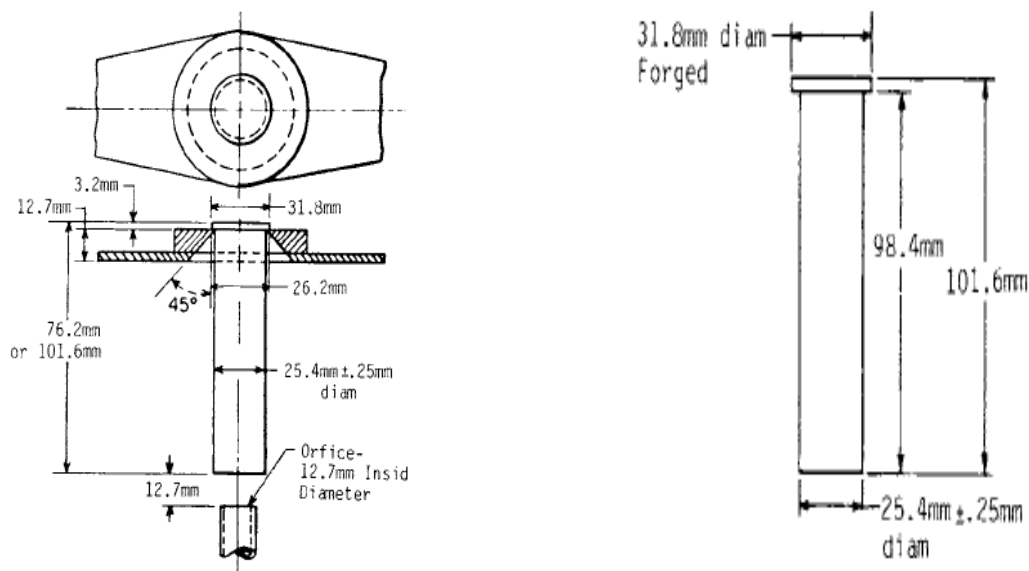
Esquema e dimensões do dispositivo de têmpera Jominy e dimensões do corpo-de-prova padrão.
